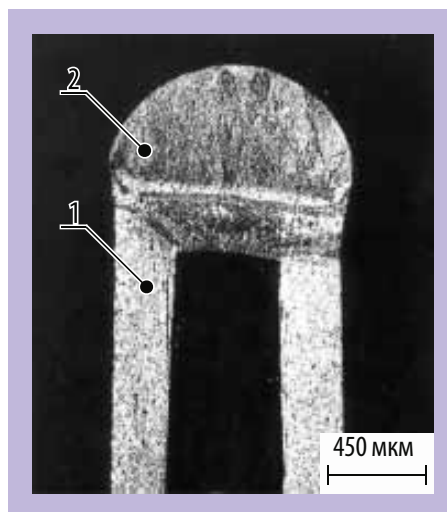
Структура сварного соединения корпуса источника: 1 — корпус, 2 — сварной шов
